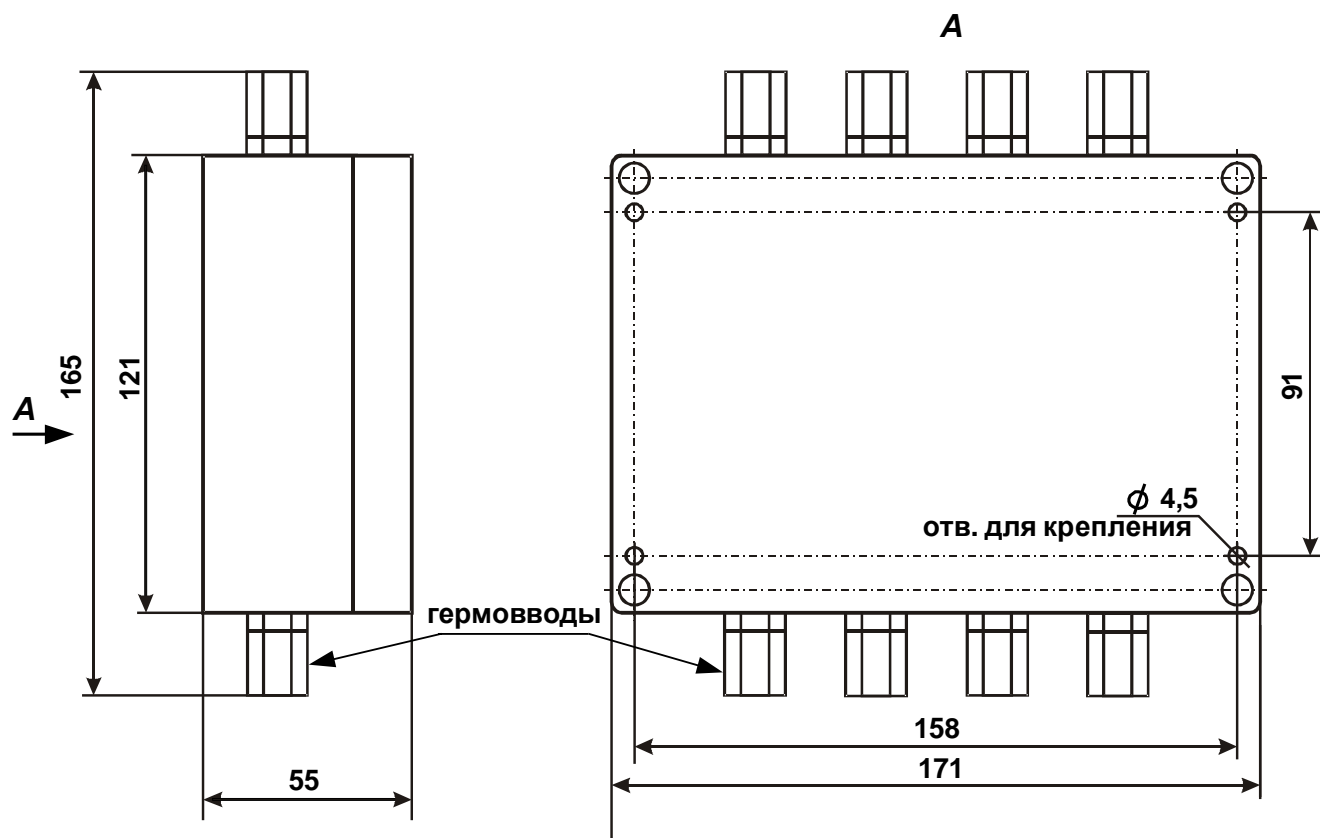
Внешний вид, габаритные и присоединительные размеры (исполнение IP65)
